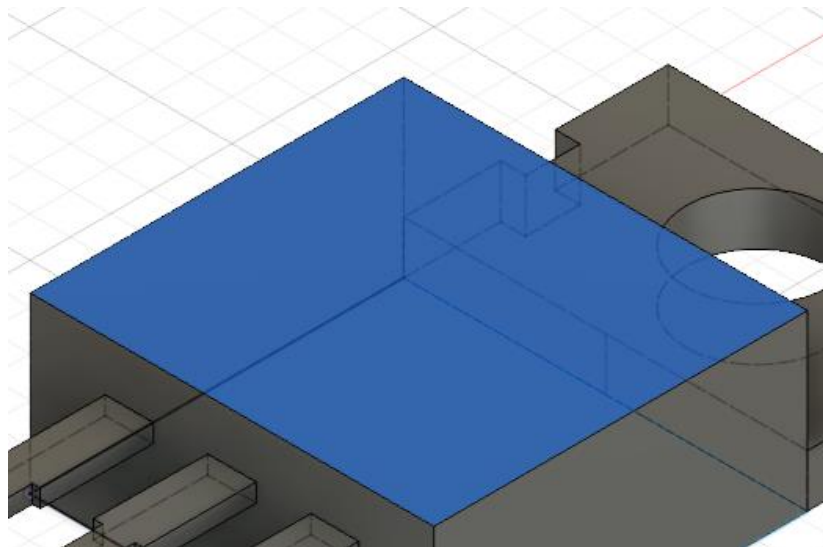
«Верхня поверхня корпусу транзистора»
